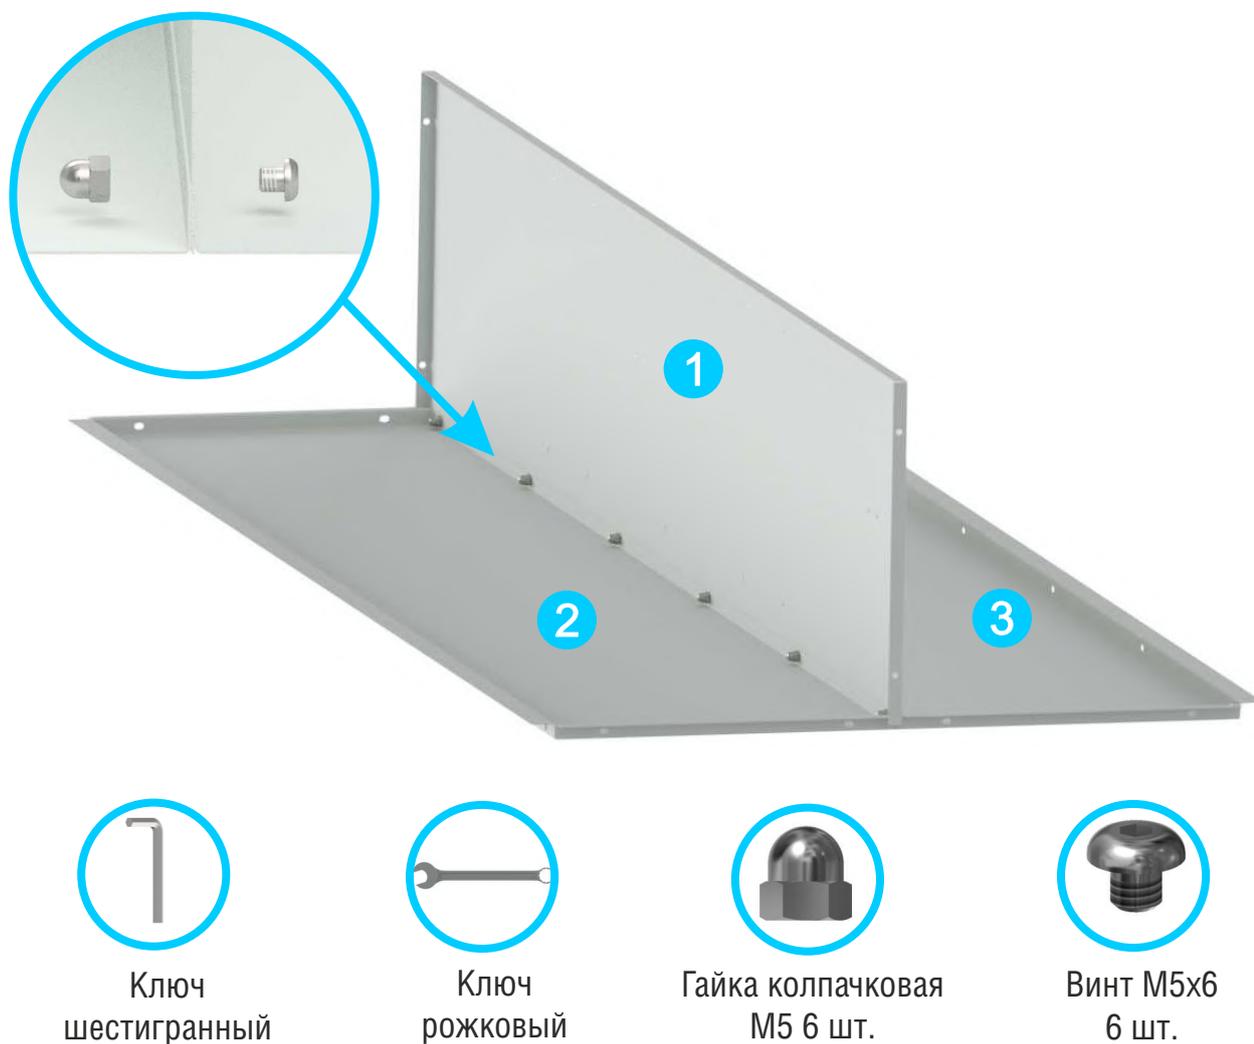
Сборка задней стенки и установка центральной перегородки.
